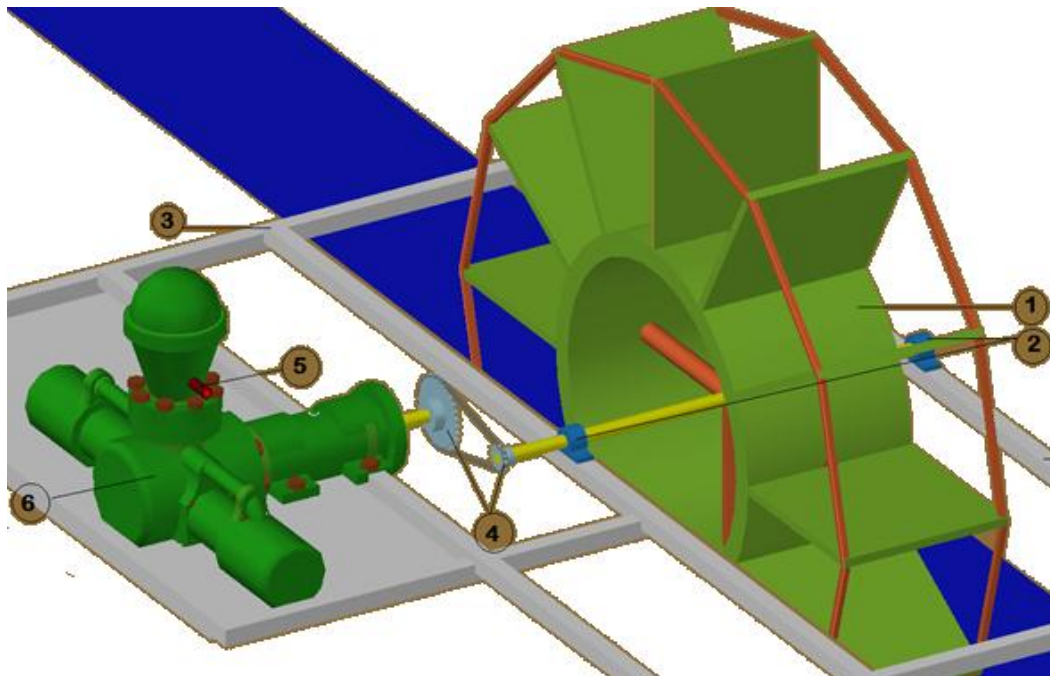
Principales componentes del conjunto Rueda- Bomba.
